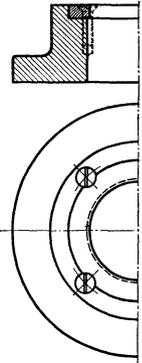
Befestigung der Schnittplatte durch Schraubenköpfe.
